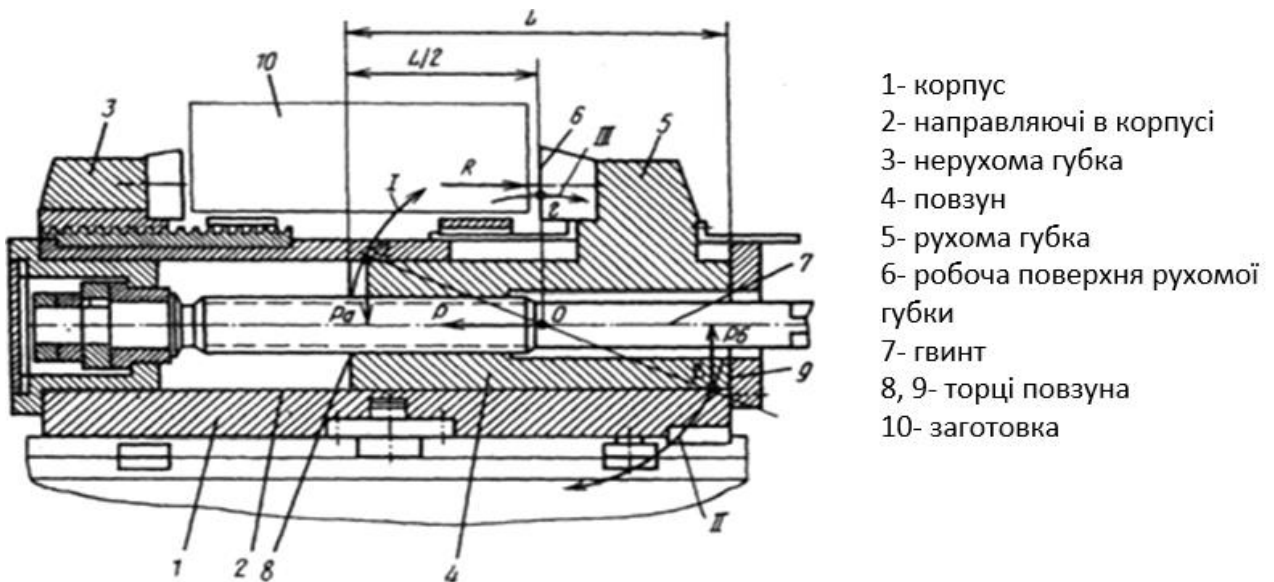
Конструкція лещат з циліндричними направляючими
